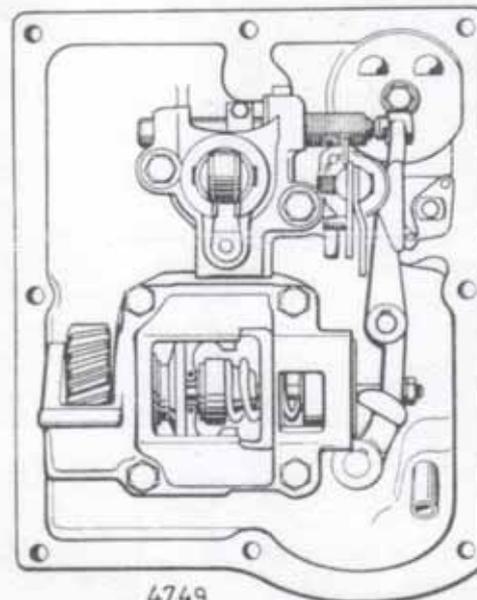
Rückansicht Gehäusedeckel mit Einspritzpumpe und Regler F 1L 712
